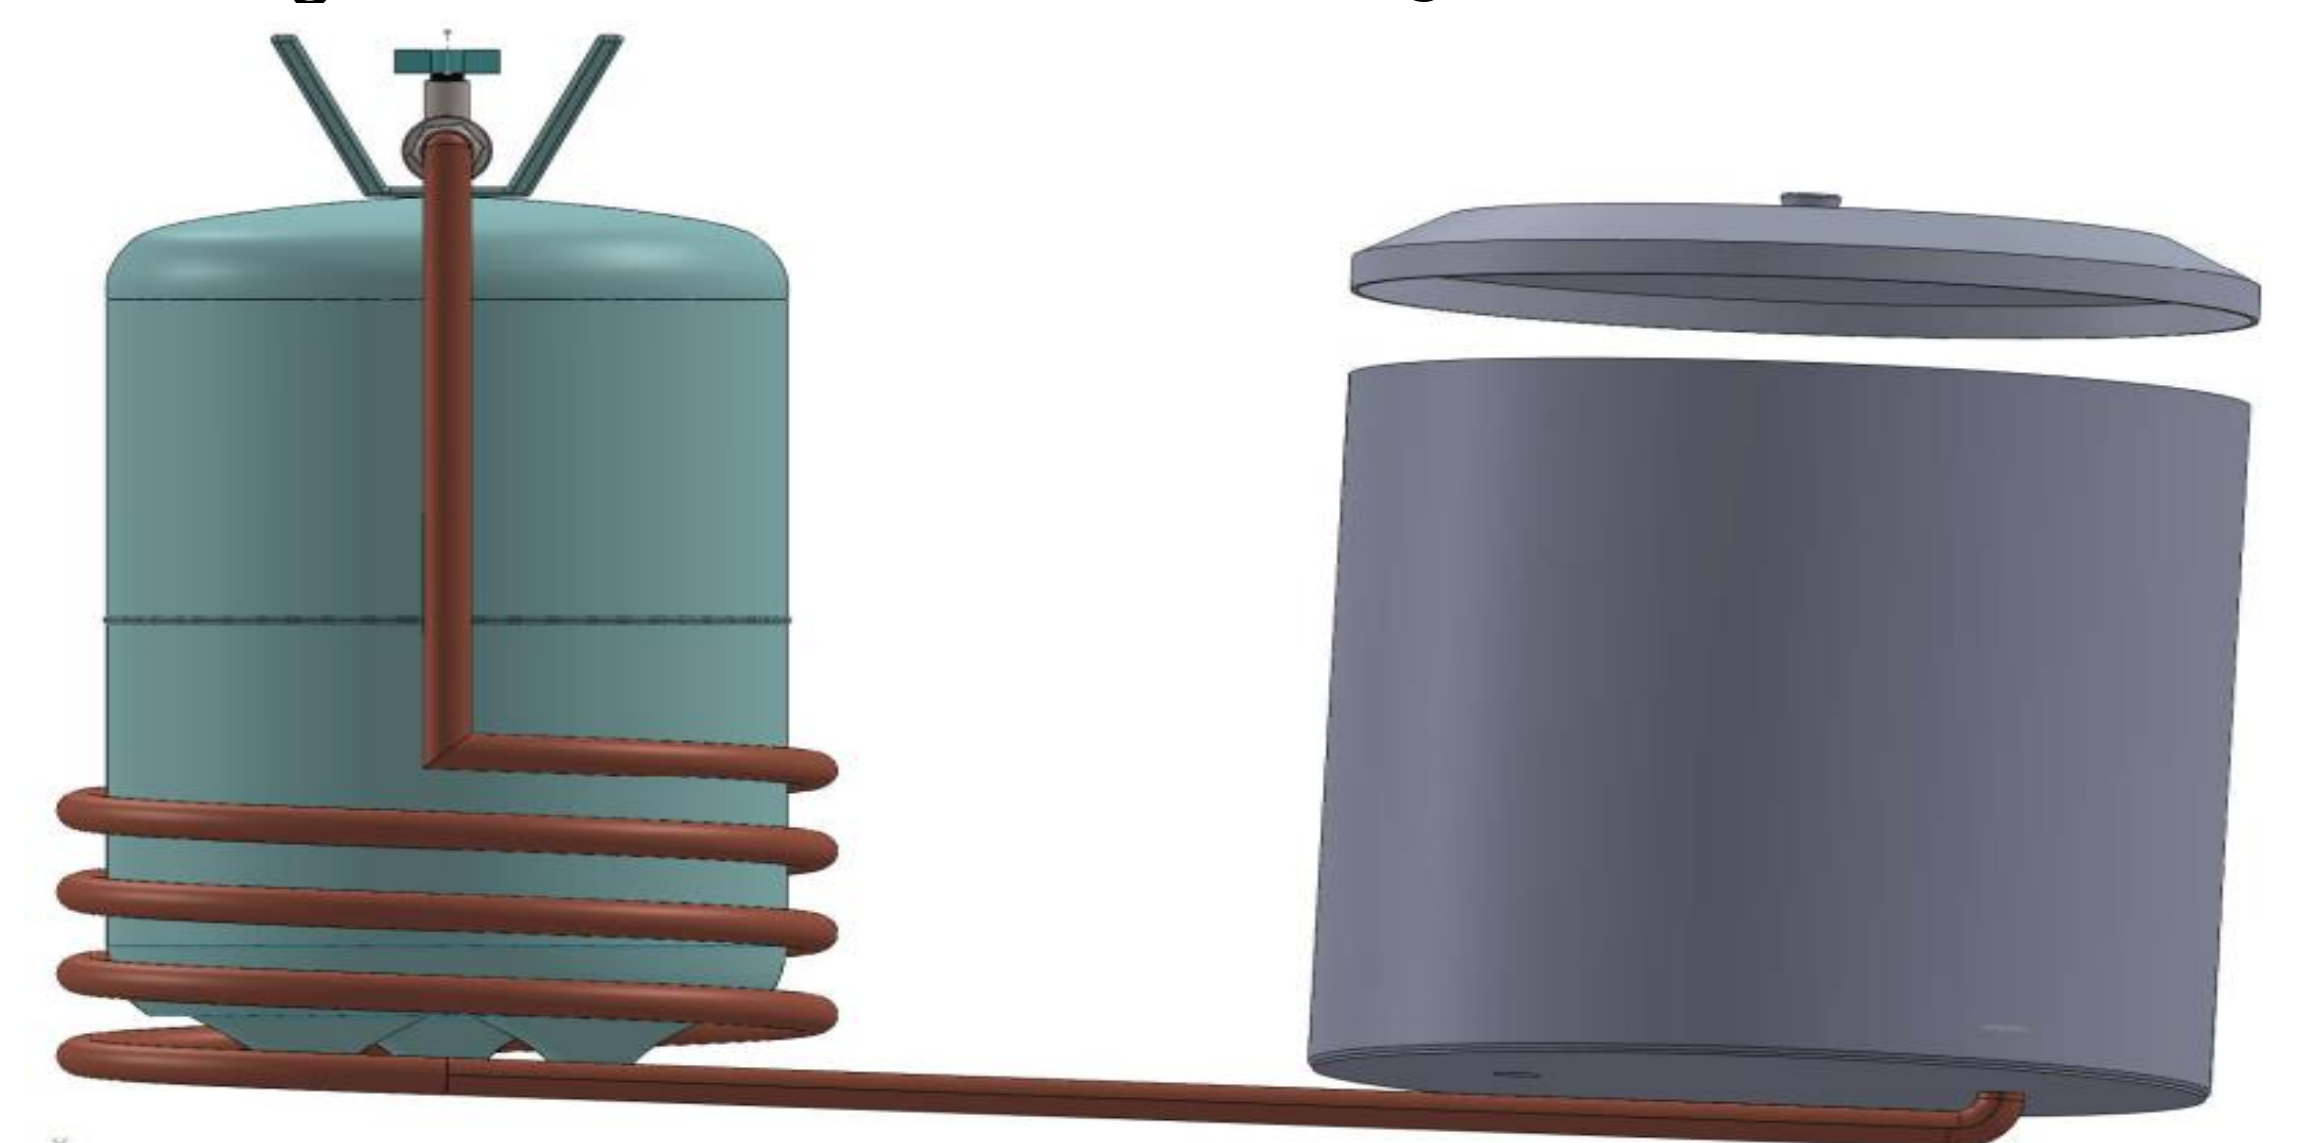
Vue 3D du dessin d'ensemble de l'étuveuse à vapeur
